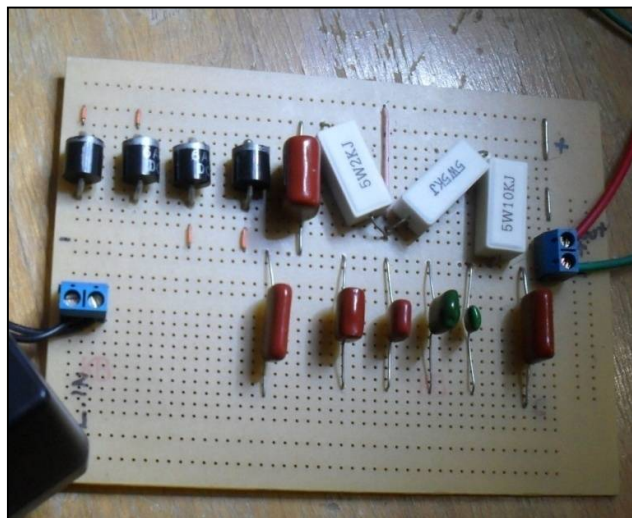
Circuito para la soldadura de μ TC por descarga de condensadores.
